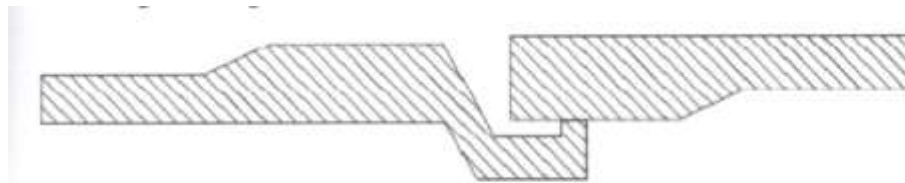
Beispiel für eine Schweißbadsicherung
